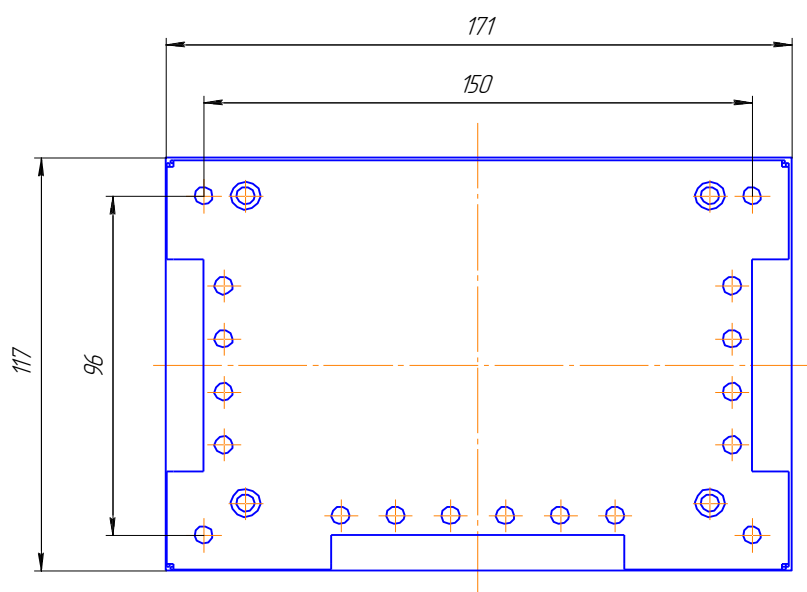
Разметка крепления АМЗ в металлическом корпусе.
